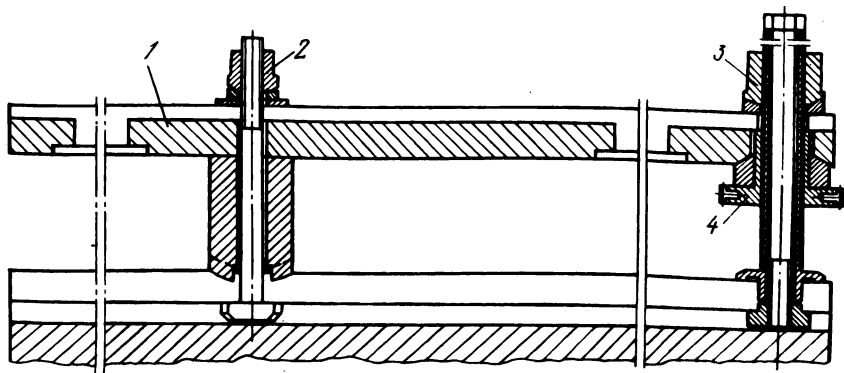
Конструкция приспособления к заточному станку для установки оси инструмента в вертикальной плоскости.
